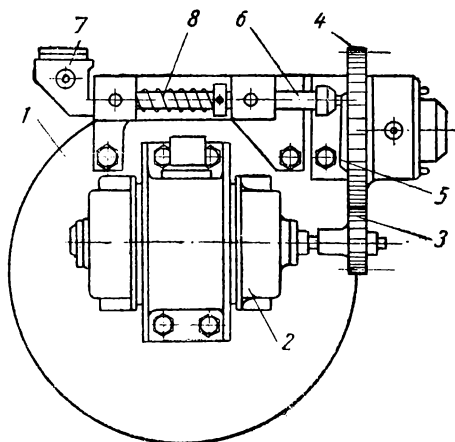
Универсальное приспособление для шлифования направляющих станин токарных станков:
